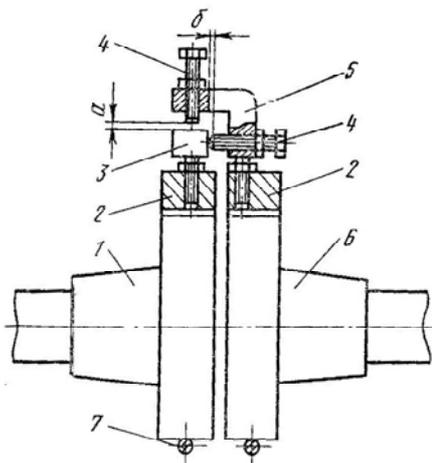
Схема проверки установки электродвигателя и компрессора:
